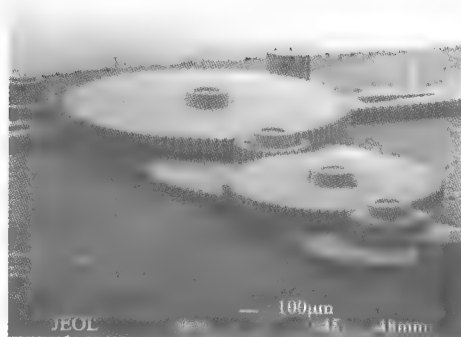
装配好的两层 78/22 镍铁合金制作的齿轮机构。铝基版上用常规采用的压式钢针, 以便于齿轮的安装
